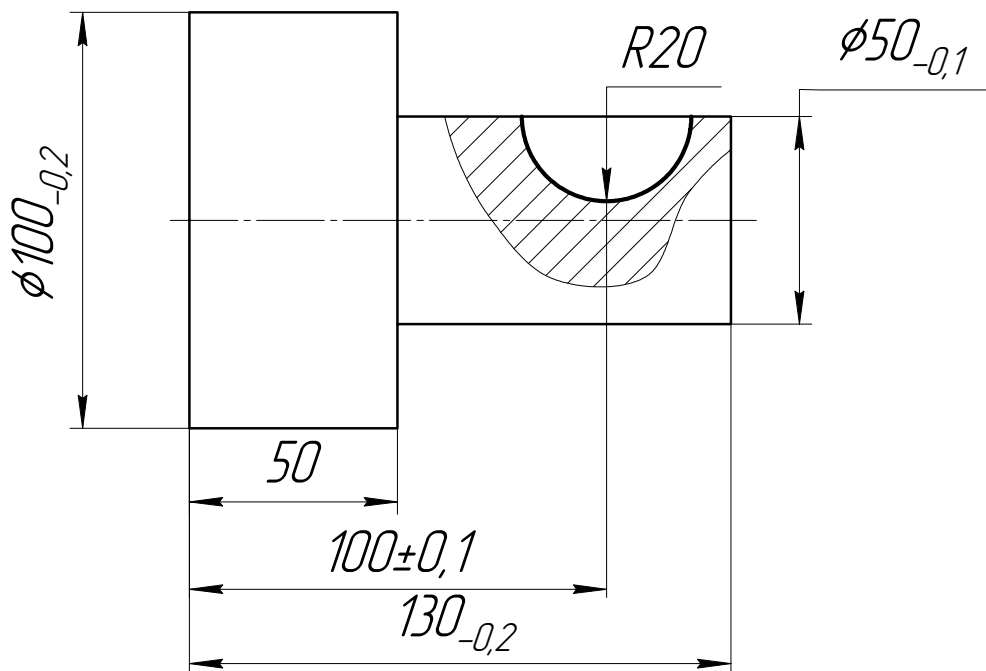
Фрезерование шпоночных канавок дисковыми фрезами
